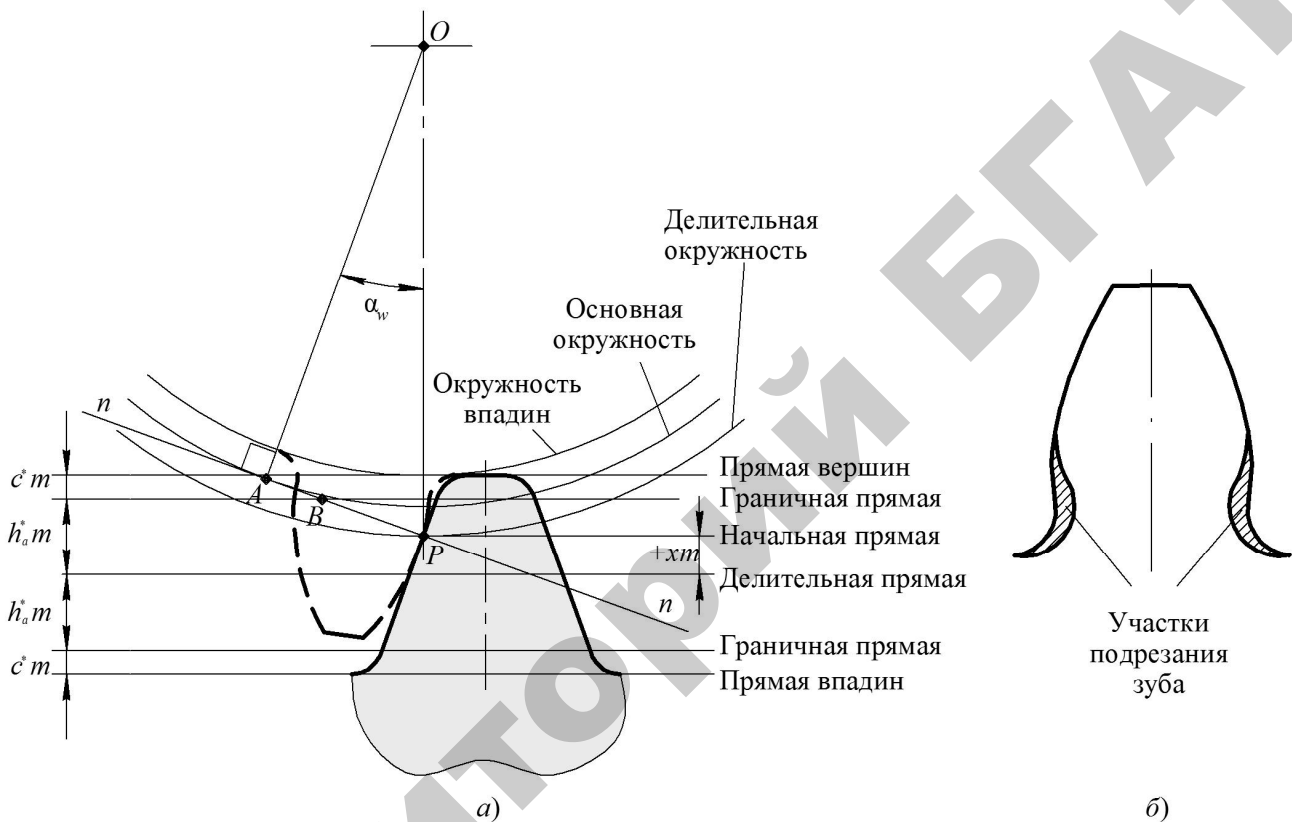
Схема к описанию явления подрезания зуба зубчатого колеса
